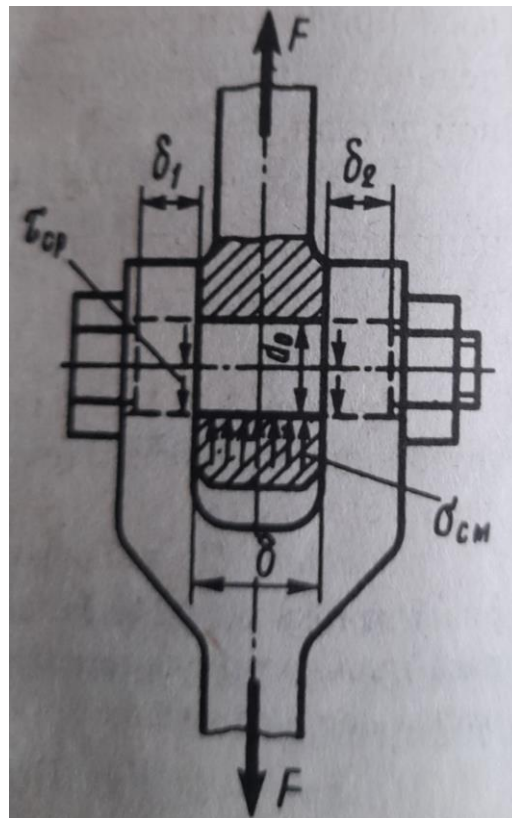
Расчетные схемы болтовых соединений без зазора, нагруженных поперечной силой
